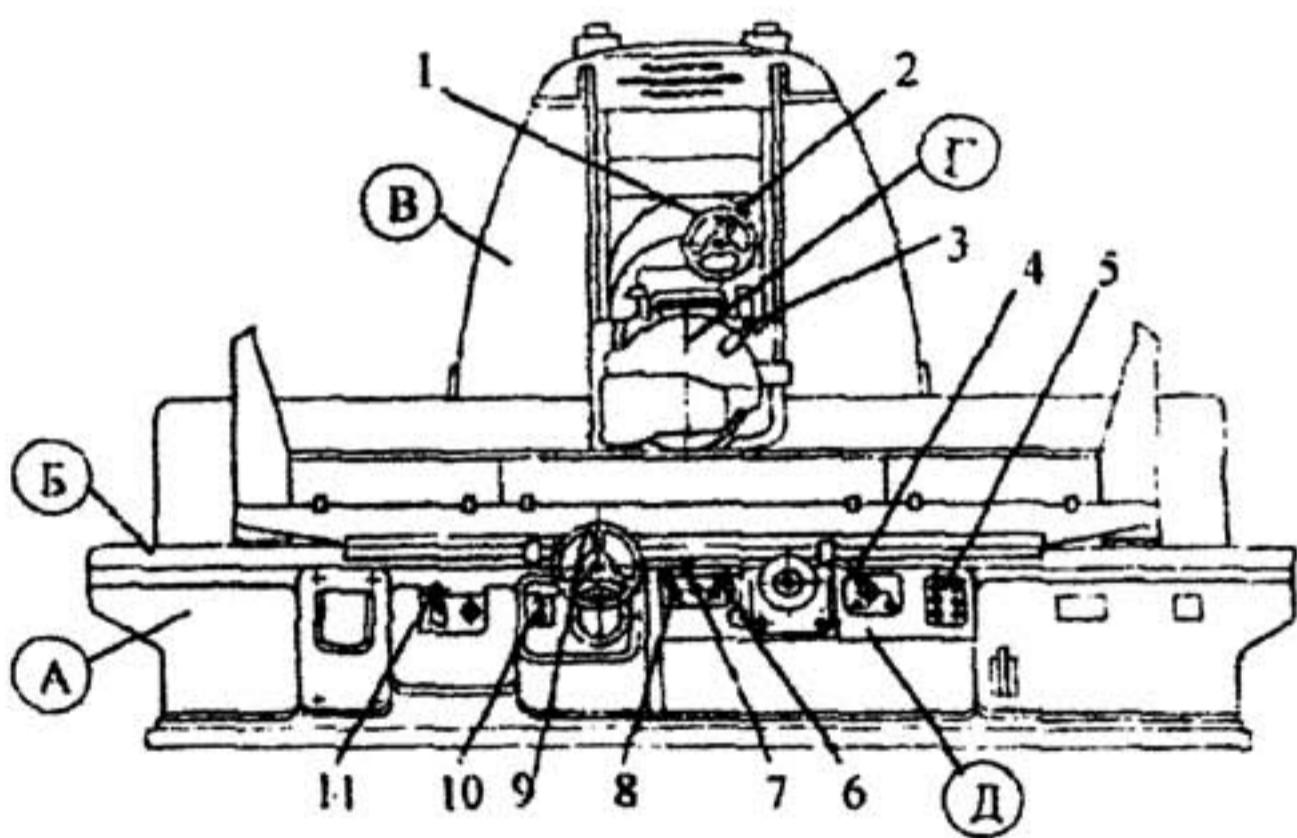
Общий вид плоскошлифовального станка мод. 3Б754
